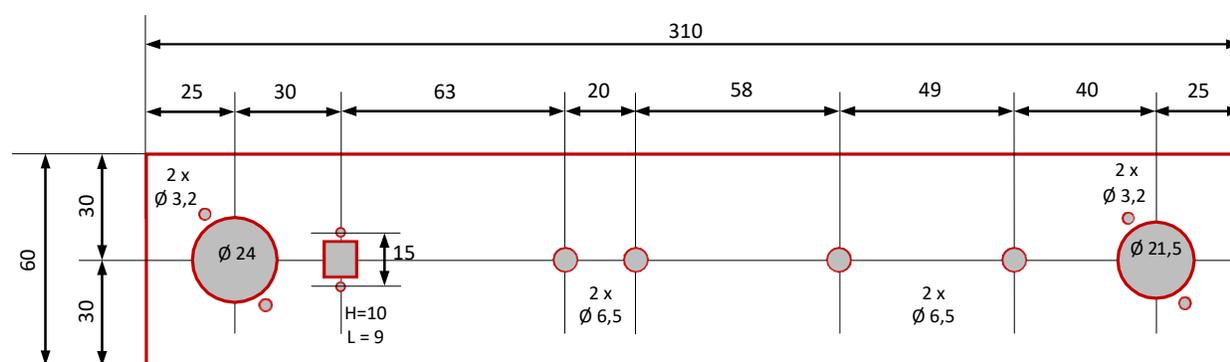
plan de l'usinage de la face arrière – Échelle ½
